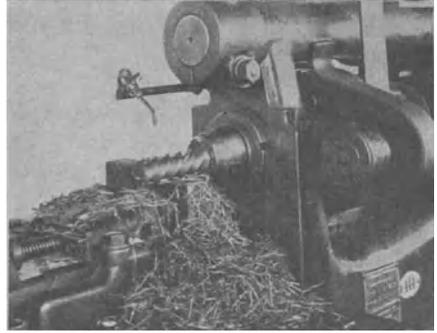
Auch alte Maschinen arbeiten wieder wirtschaftlich, wenn ein leicht schneidender Fräser benutzt wird.
